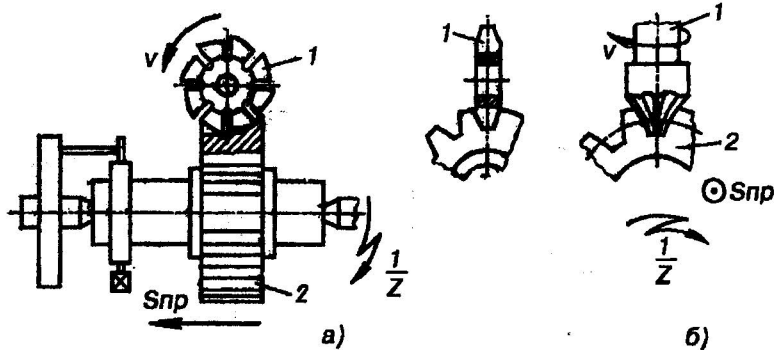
Схеми фрезерування зубців за методом копіювання:
